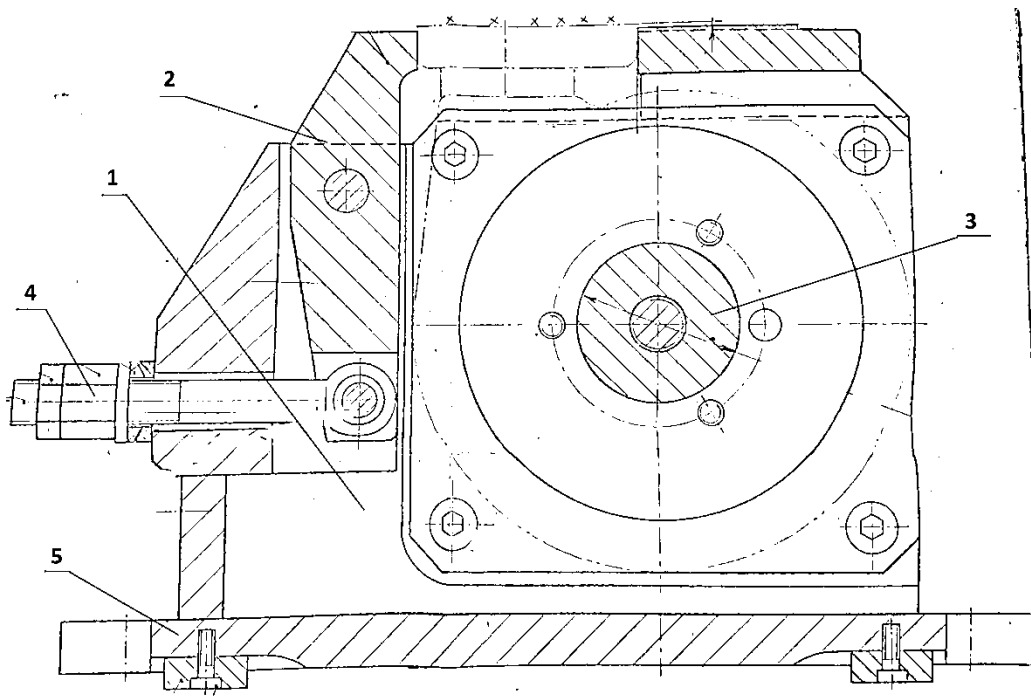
Приспособление фрезерное. Главный вид: 1 – Корпус, 2 – Прихват, 3 – Палец , 4 – Гайка, 5 – Установочная плита.
